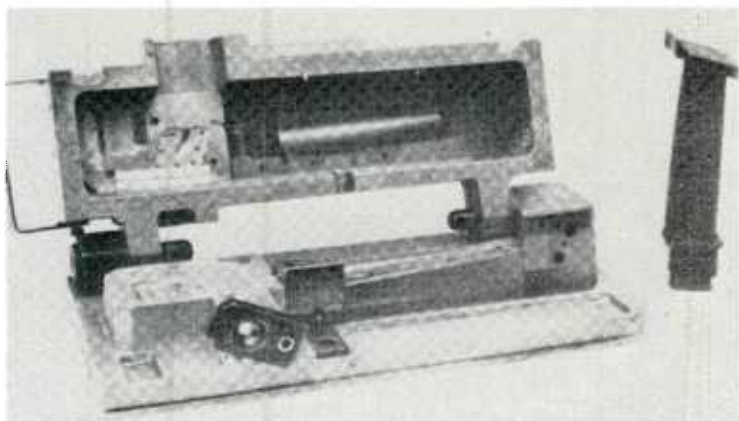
Outillage injection de cire pour aube mobile de turbine.
